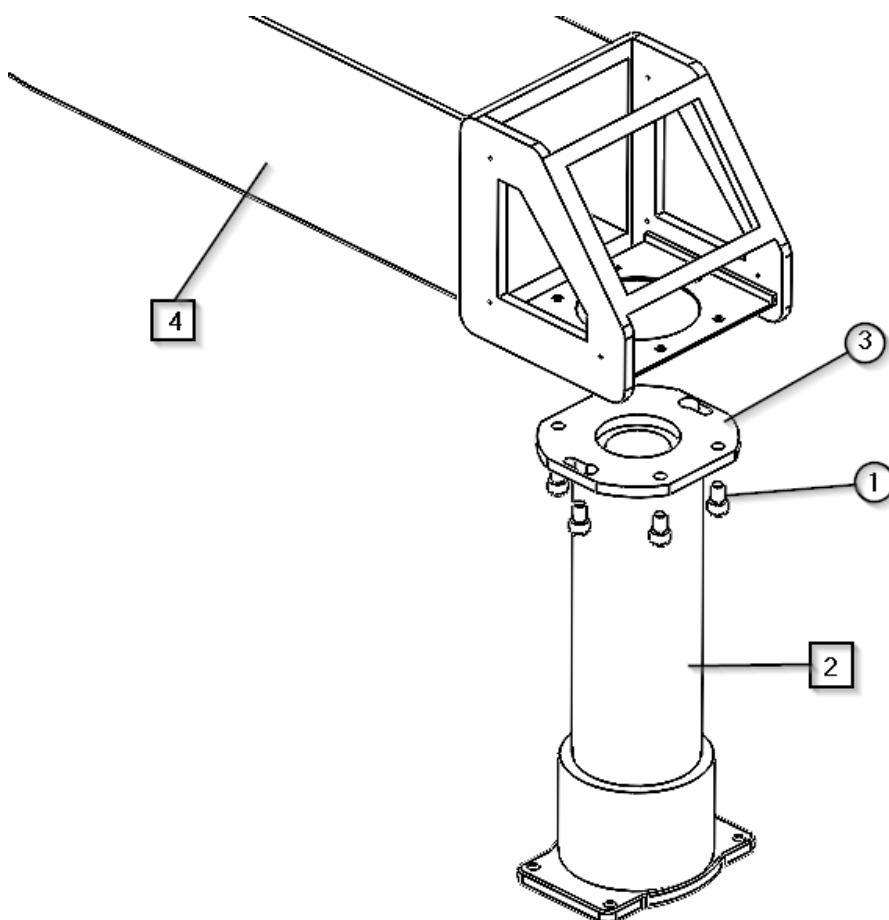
Montaje tubo de caída sobre brazos motorizados
